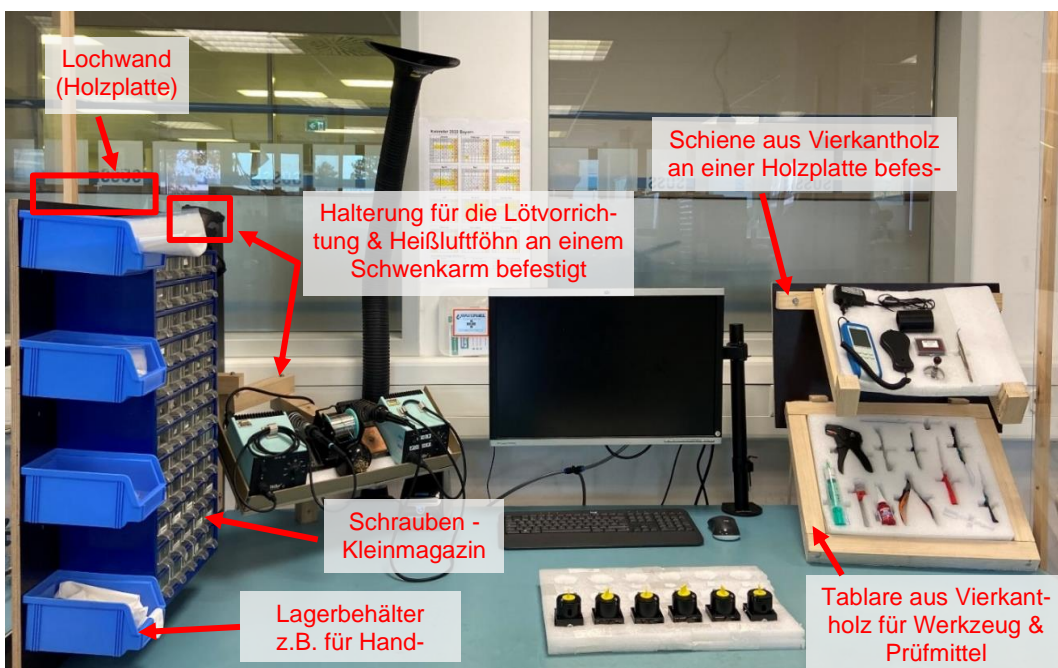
optimierter Montagearbeitsplatz inkl Prüfplatz
